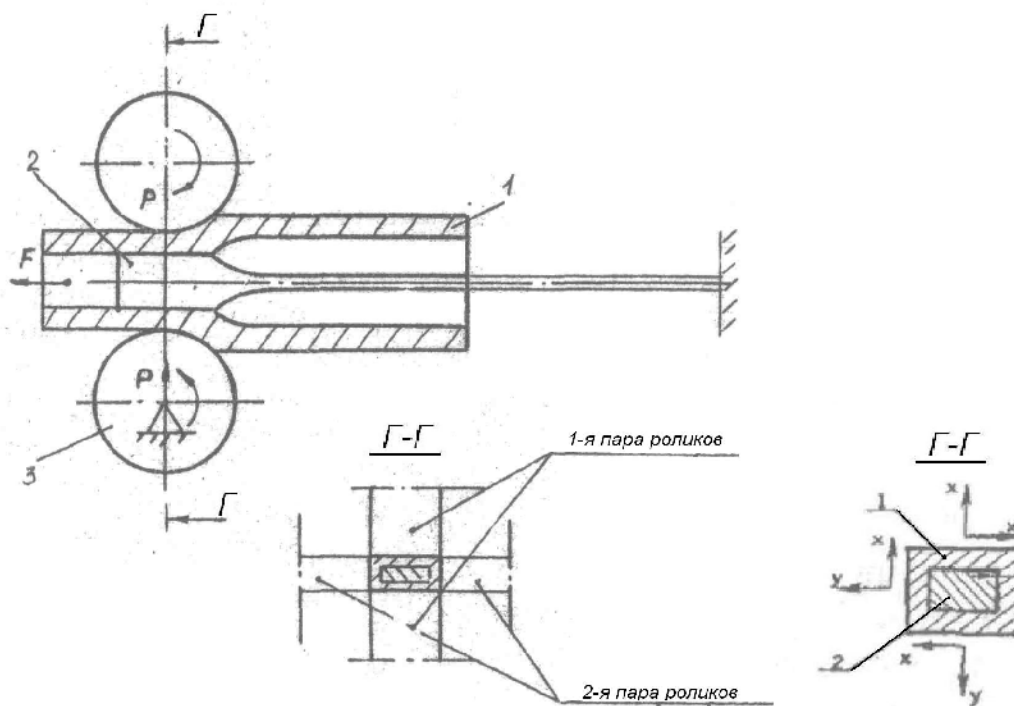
Схема процесса изготовления прямоугольного волновода ППФ из сплава 32НКД методом многостороннего деформирования: 1 – трубчатая заготовка волновода; 2 – инструмент-дорн; 3 – ролики роликковой фильеры
